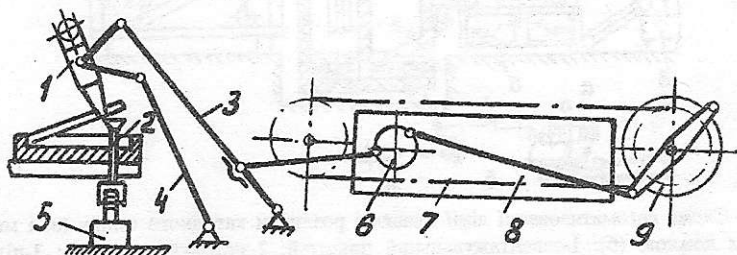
Схема анодознімача: 1-захват; 2-шттовхач з роликом; 3-підтримуючий важіль; 4-приводний важіль; 5-копір; 6-приводний кривошип; 7-ланцюгова передача; 8-ванна; 9-храпове зачеплення
